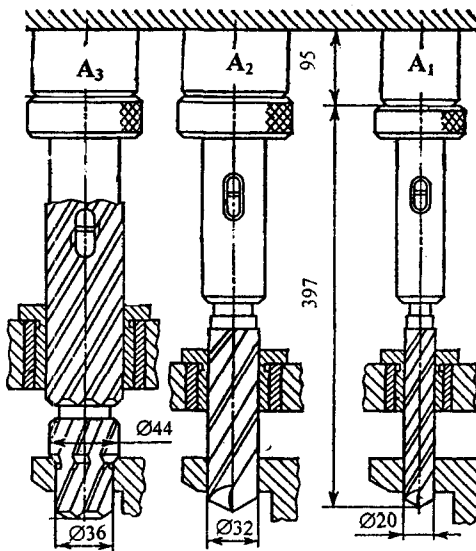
Схема обробки заготовки на агрегатному вертикальному верстаті багатшпindelною головкою.
